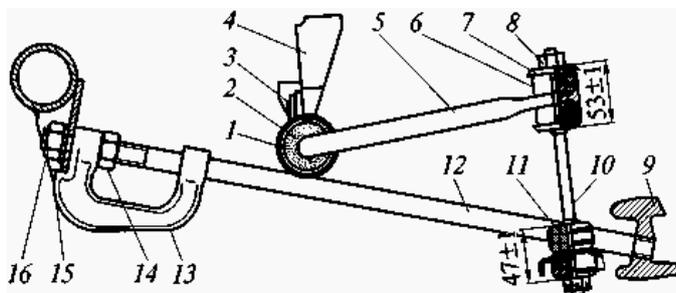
Стабилизатор передней подвески: 1 — обойма; 2 — резиновая втулка; 3 — болт; 4, 15 — кронштейны; 5 — штанга; 6 и 11 — верхняя и нижняя резиновые подушки; 7 — чашка; 8, 16 — гайки; 9 — поперечина подвески; 10 — стойка; 12 — растяжка передней подвески; 13 — буксирная скоба; 14 — контргайка
